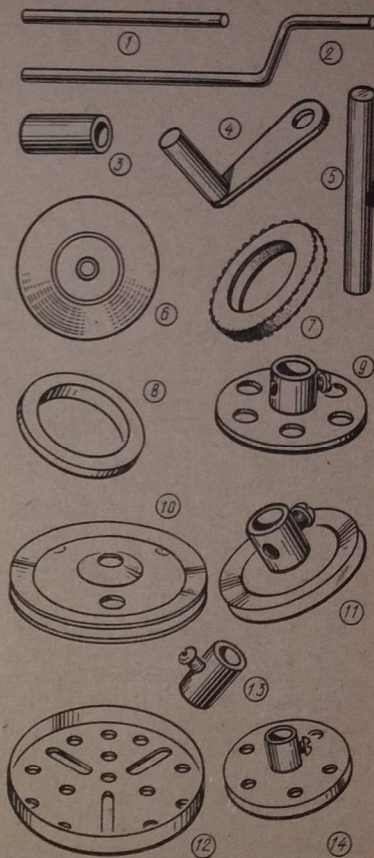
Детали вращения: 1 — осевой стержень; 2 — заводная рукоятка; 3 — втулка; 4 — ручка; 5 — вал; 6 — колесо; 7 — автомобильная шина; 8 — резиновое кольцо; 9 — планшайба с втулкой; 10 — ролик без ступицы; 11 — ролик со ступицей; 12 — диск; 13 — кольцо; 14 — колесо
